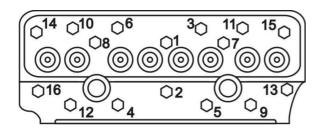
Схема затяжки болтов крепления головки цилиндров
